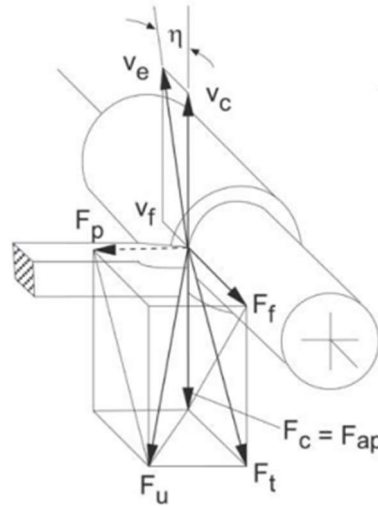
Forças de usinagem (DINIZ et al., 2001)
